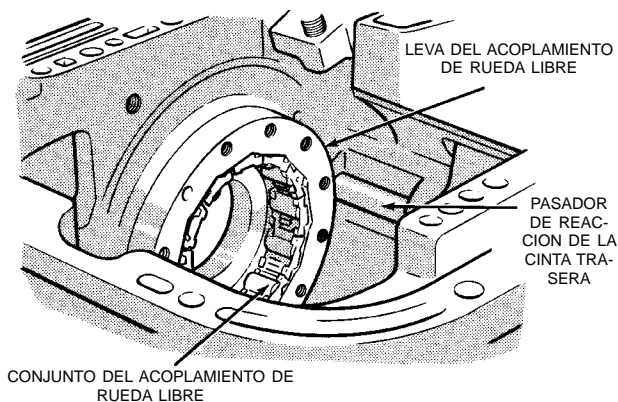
Desmontaje del conjunto del acoplamiento de rueda libre
